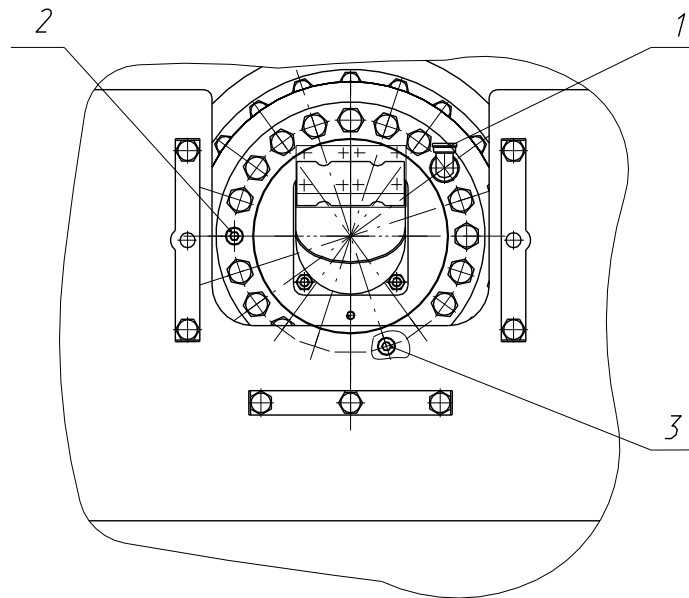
Схема заправки планетарного редуктора привода пневмоколес
